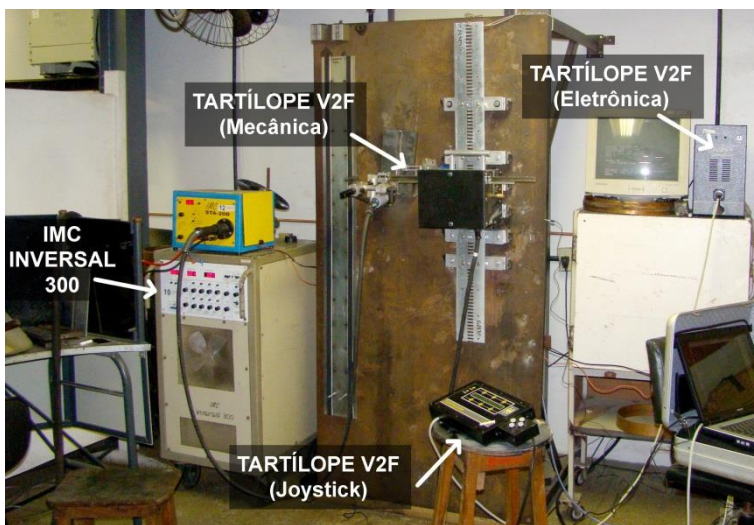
Equipamentos empregados na soldagem com o manipulador TARTÍLOPE V2F.
